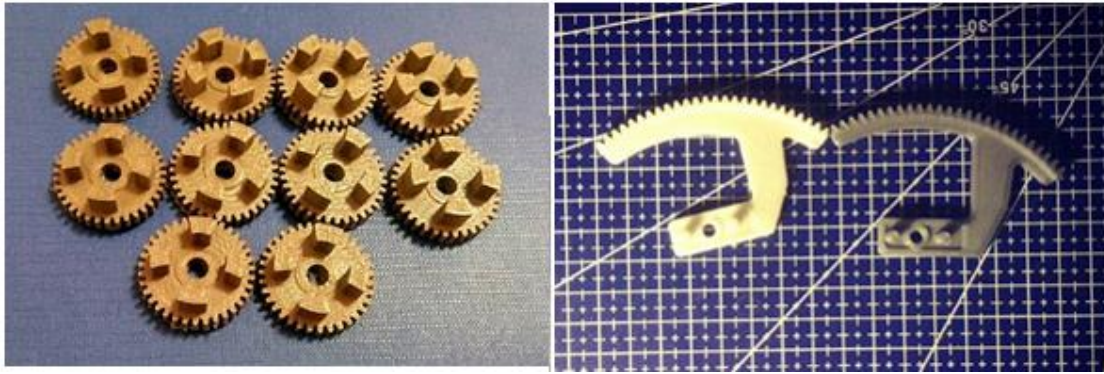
Деталі рухомих з'єднань, виготовлені за допомогою 3D друку
